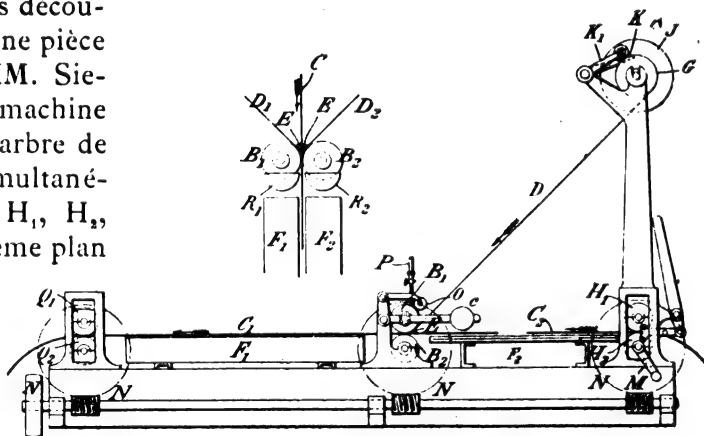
et 2. — Machine à coller Siemens Brothers.
